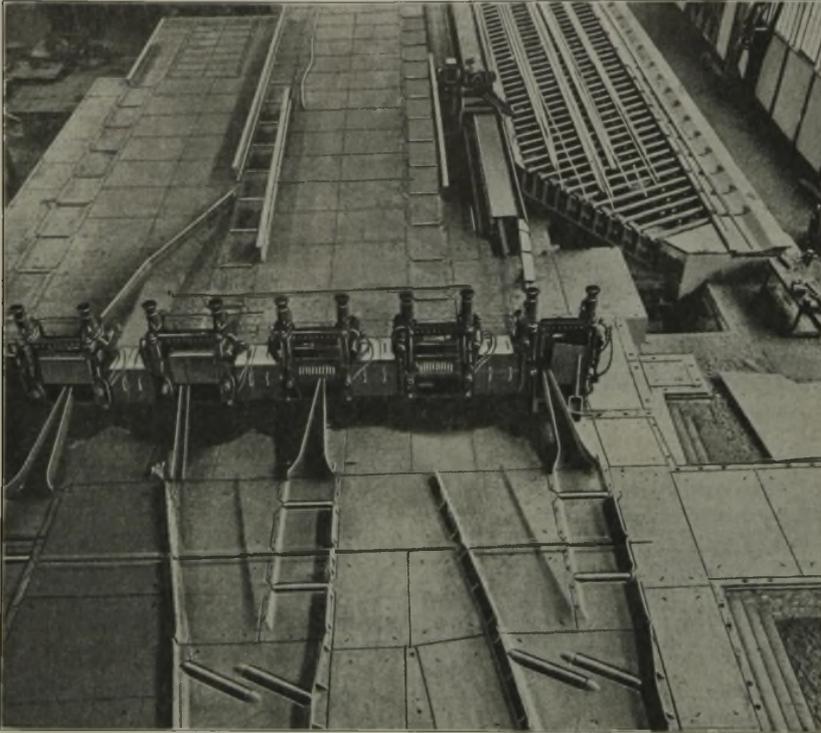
360er Fertigstraße mit Rollgängen und Kühlbett.
